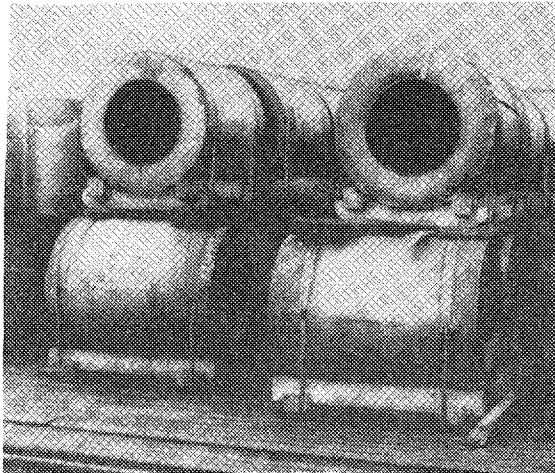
Складирование стального листа в рулонах на "салазках"
